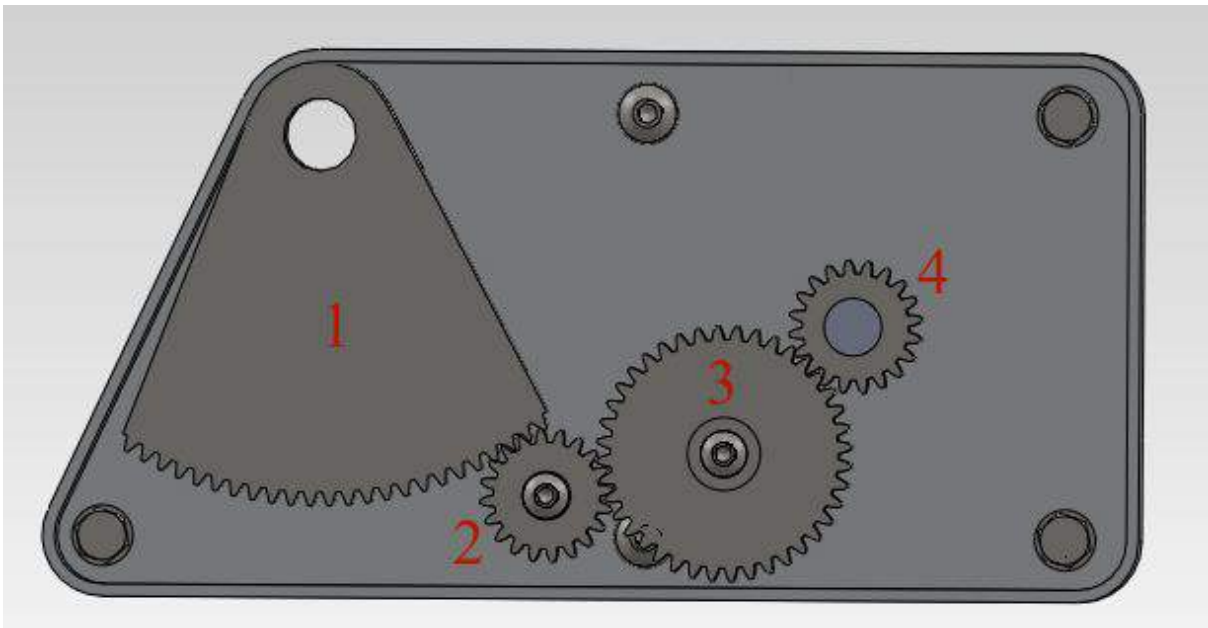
Disposición engranajes dentro de la reductora del eje horizontal.
